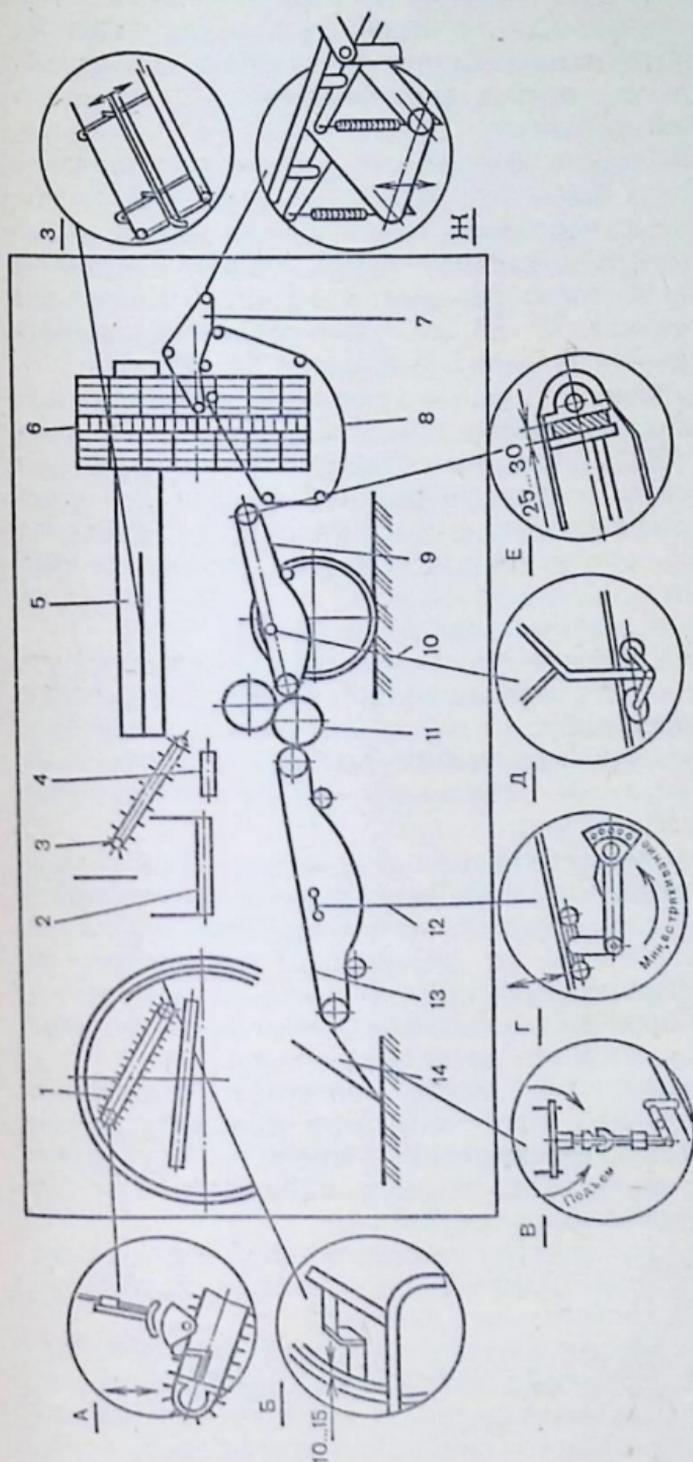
Основные регулировки картофелеуборочного комбайна ККУ-2А:
